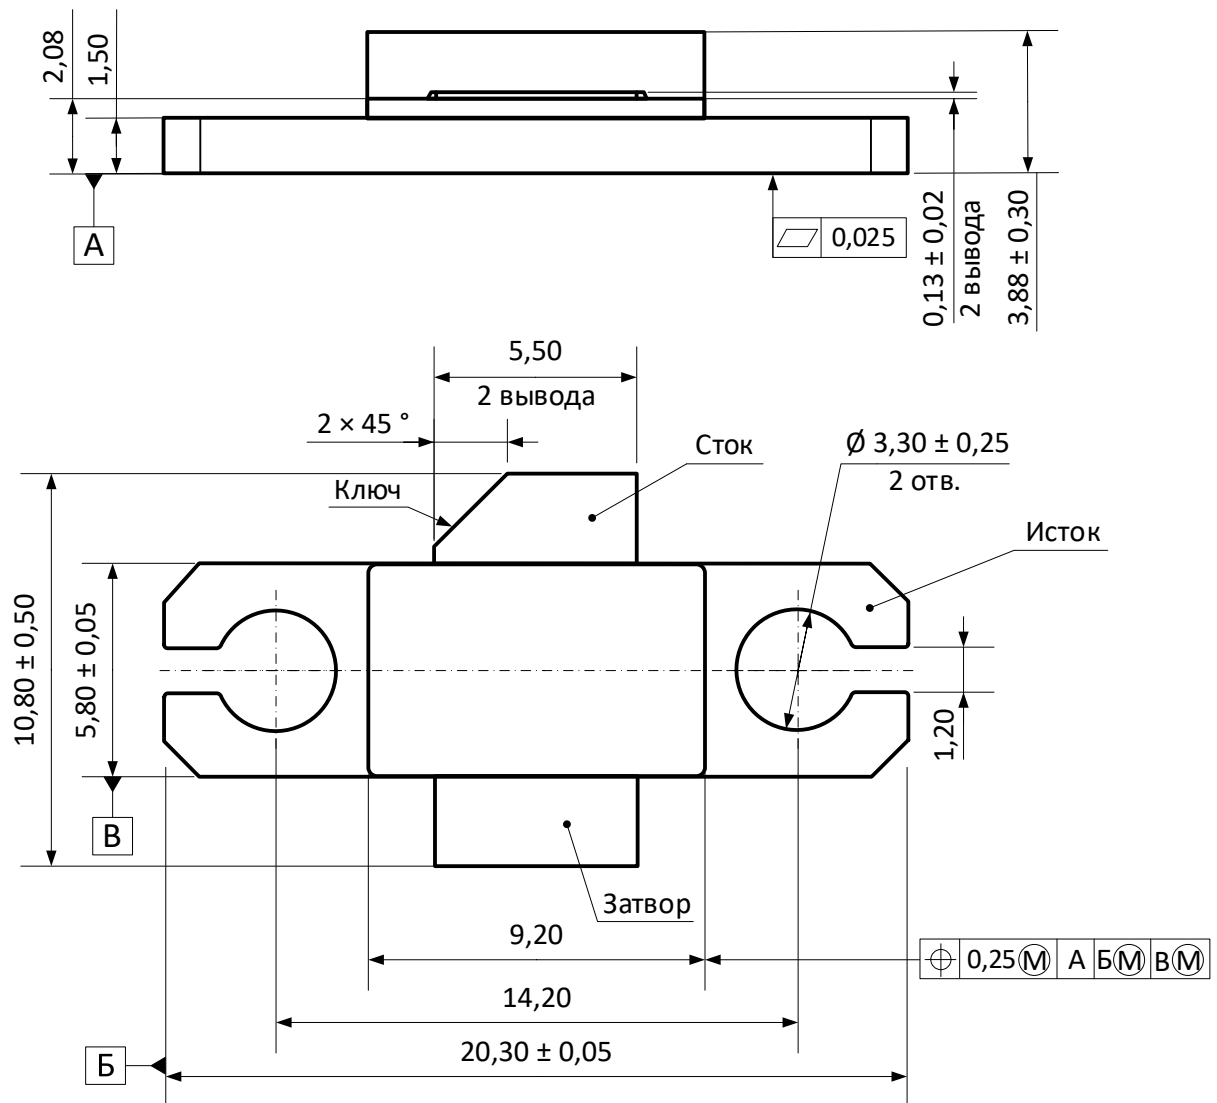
Габаритный чертеж транзисторов MGN31-70A
